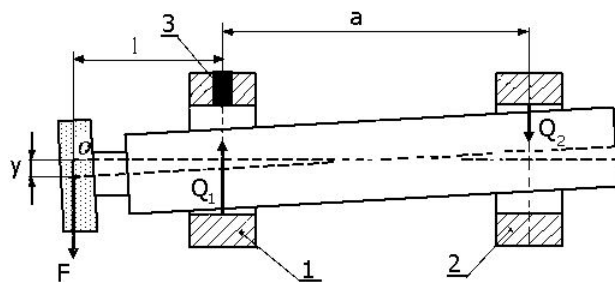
Схема шпиндельного узла: 1 – передний газоманитный подшипник; 2 – задний газостатический подшипник; 3 – магнитопровод соленоида
